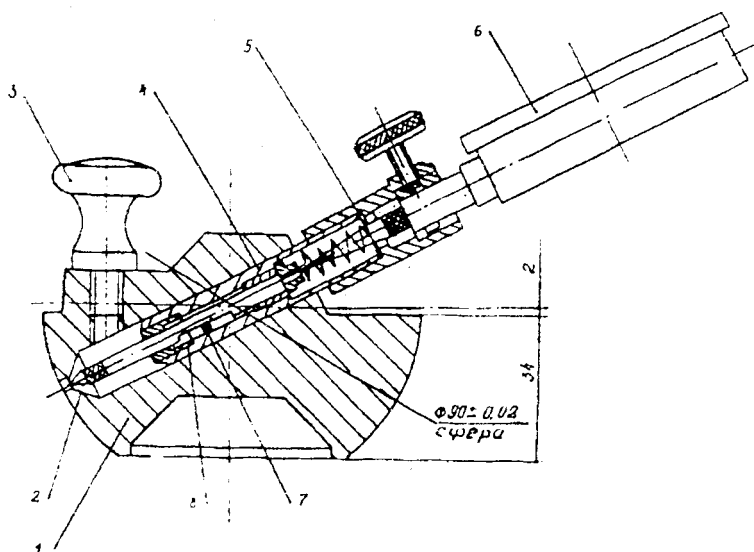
Приспособление для контроля формы открытой внутренней сферической поверхности
